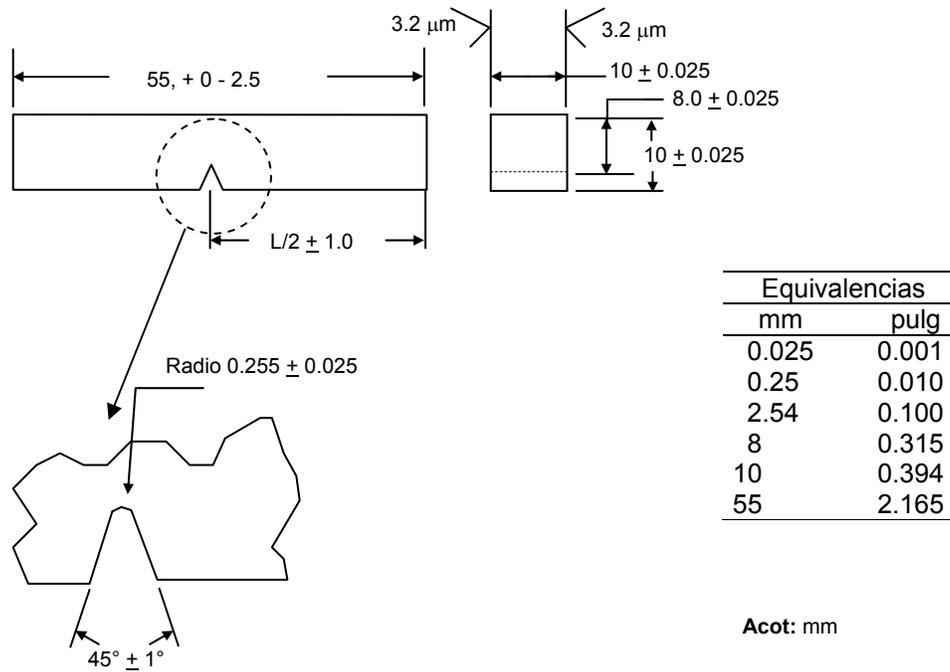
DIMENSIONES DE LA PROBETA DE TENSIÓN
